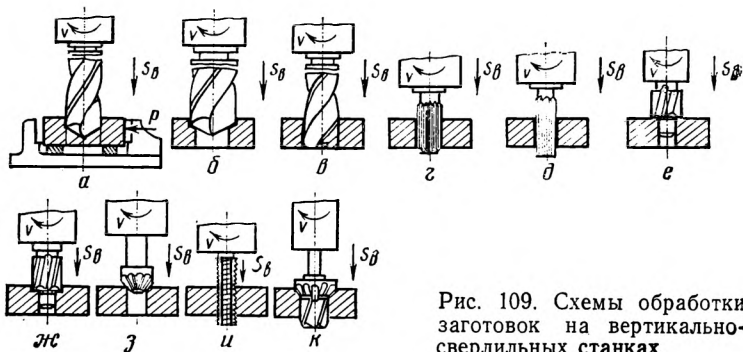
Схемы обработки заготовок на вертикально-сверлильных станках
